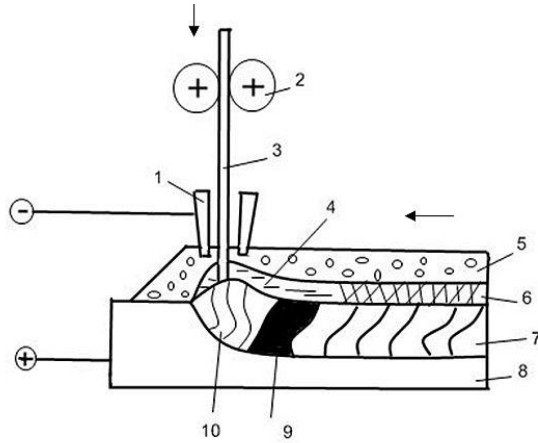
Схема автоматической дуговой сварки под флюсом. 1 – токопровод, 2 – механизм перемещения проволоки, 3 – проволока, 4 – жидкий шлак, 5 – флюс, 6 – шлаковая корка, 7 – сварной шов, 8 – основной металл заготовки, 9 – жидкий металл, 10 – электрическая дуга.
